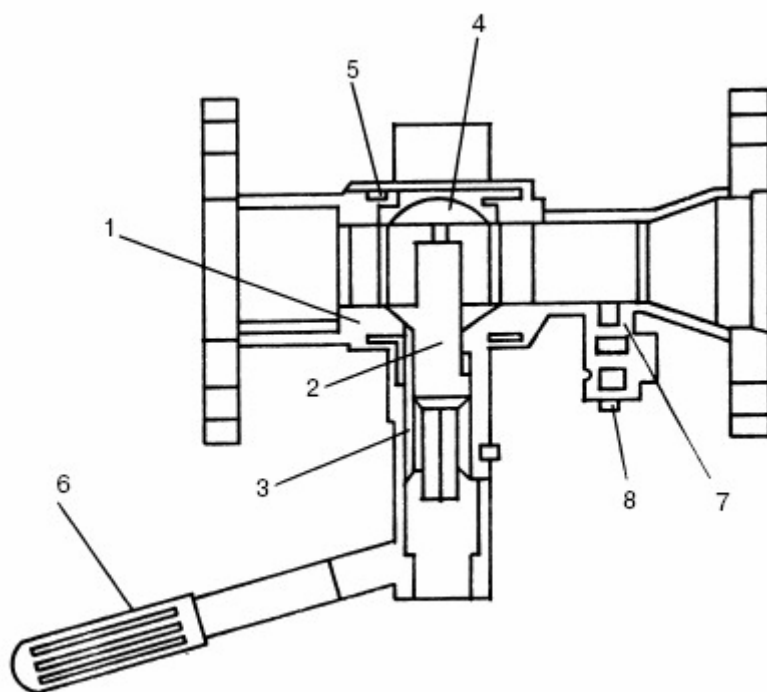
Балансировочный клапан: 1 – корпус; 2 – шток регулировочный; 3, 7 – кольцевые уплотнения; 4 – отсечной шар; 5 – седло шара; 6 – рукоятка; 8 – измерительно-дренажный патрубок
